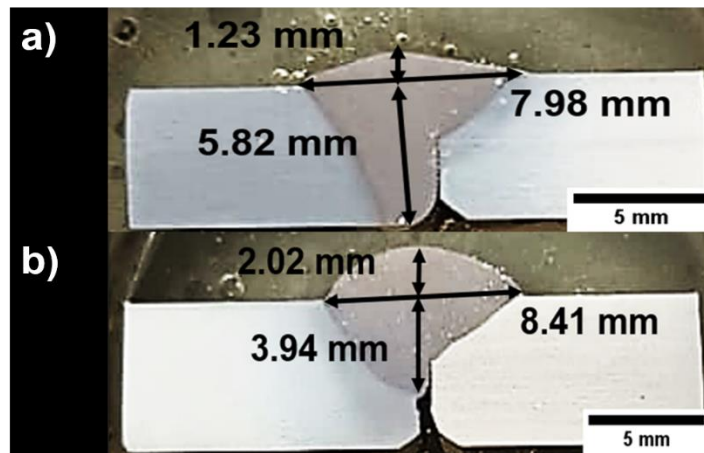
87 Unión de las placas de aleación de aluminio a) Soldadura 26 y b) réplica de la soldadura 26.
